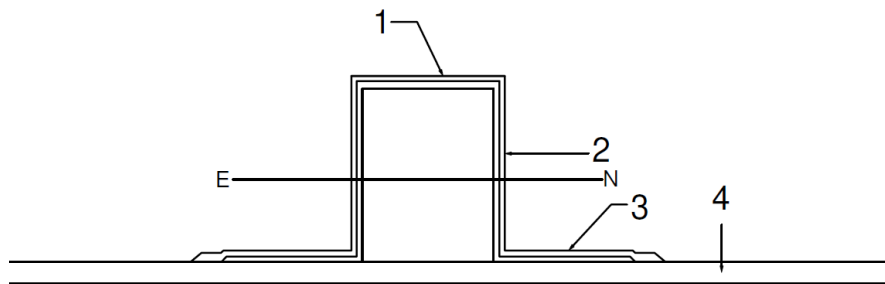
Refuerzo omega 130x130 longitudinales de fondo
